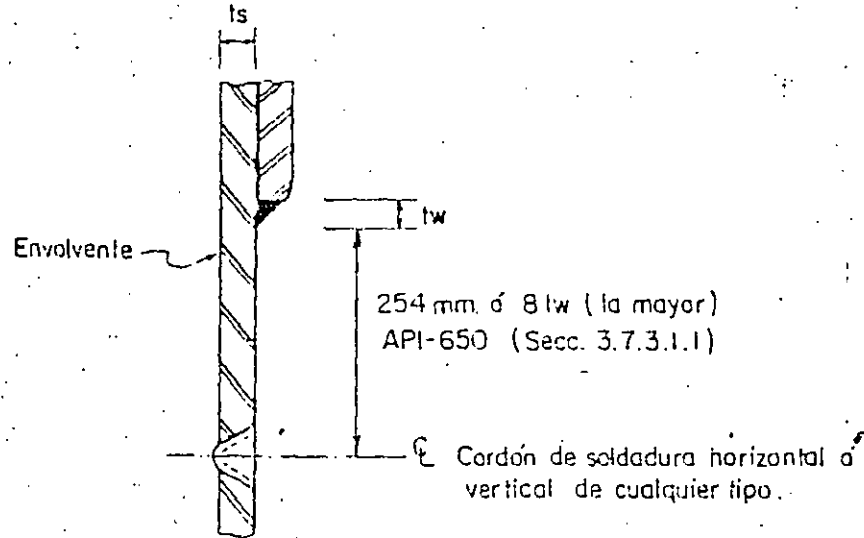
Espaciamento mínimo entre accesorios de la envoltura y cordones de soldaduras a tope de cualquier tipo.
